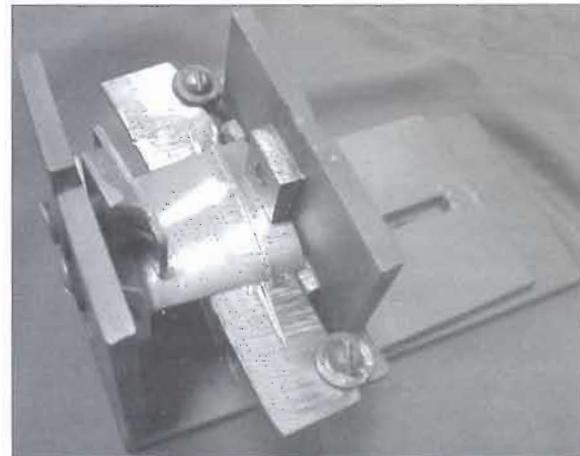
Сборочное приспособление для выполнения ЭЛС титановых лопаток
